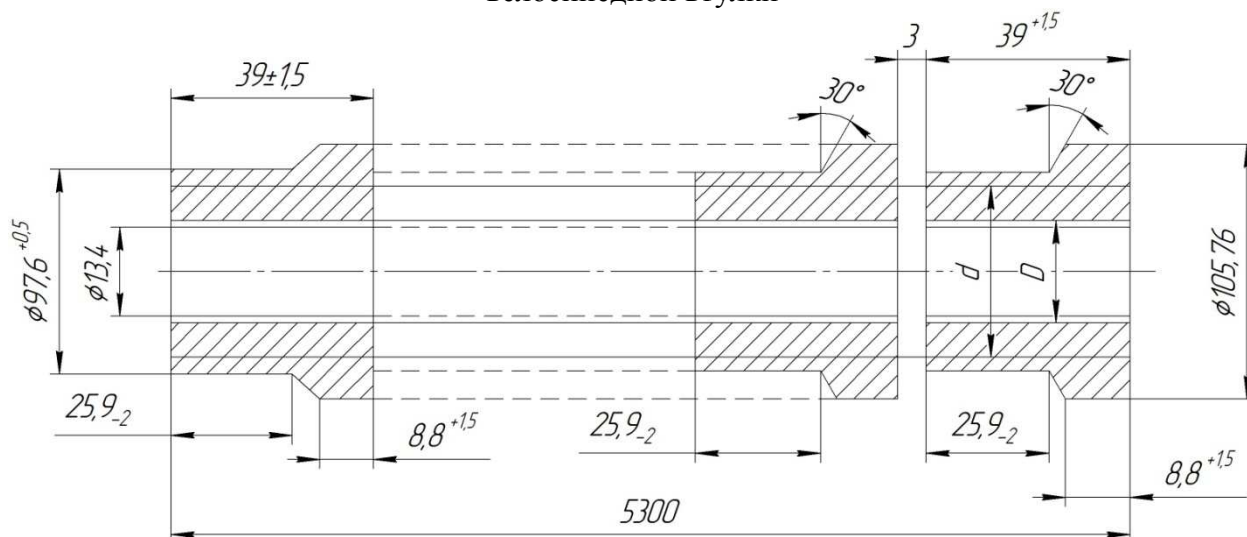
Операционный эскиз длиномерной трубной заготовки (ДТЗ) с РПП и припусками под механическую обработку ВК: L = 5300 – длина заготовки с РПП; 97,6+0,5 – диаметр наружной поверхности РПП; 73,4- диаметр прошито отверстия; 8,5+1,5 – размер длины бурта; 25,9-2 – линейный размер заготовки под дорожку качения; 3- размер припуска под отрезку заготовки ВК отрезным резцом; 3° –угол наклона бурта
